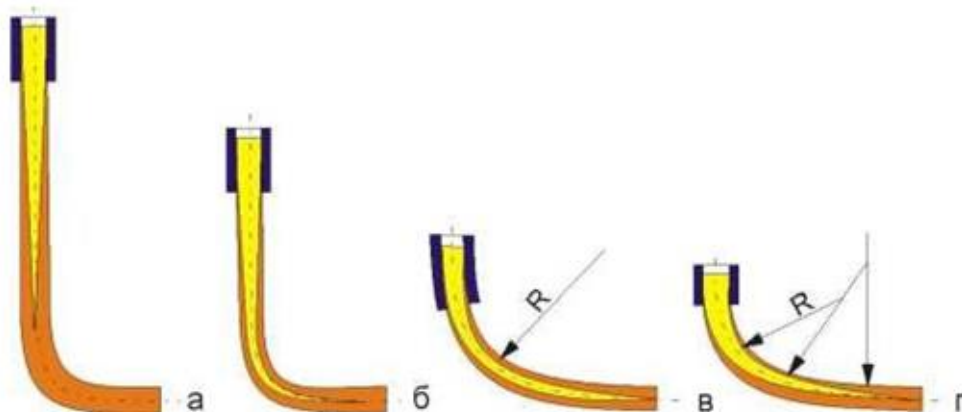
МНЛЗ с криволинейной технологической осью: а — изгиб затвердевшей заготовки, б — изгиб заготовки с жидкой сердцевиной, в — радиальный изгиб, г — криволинейный изгиб
